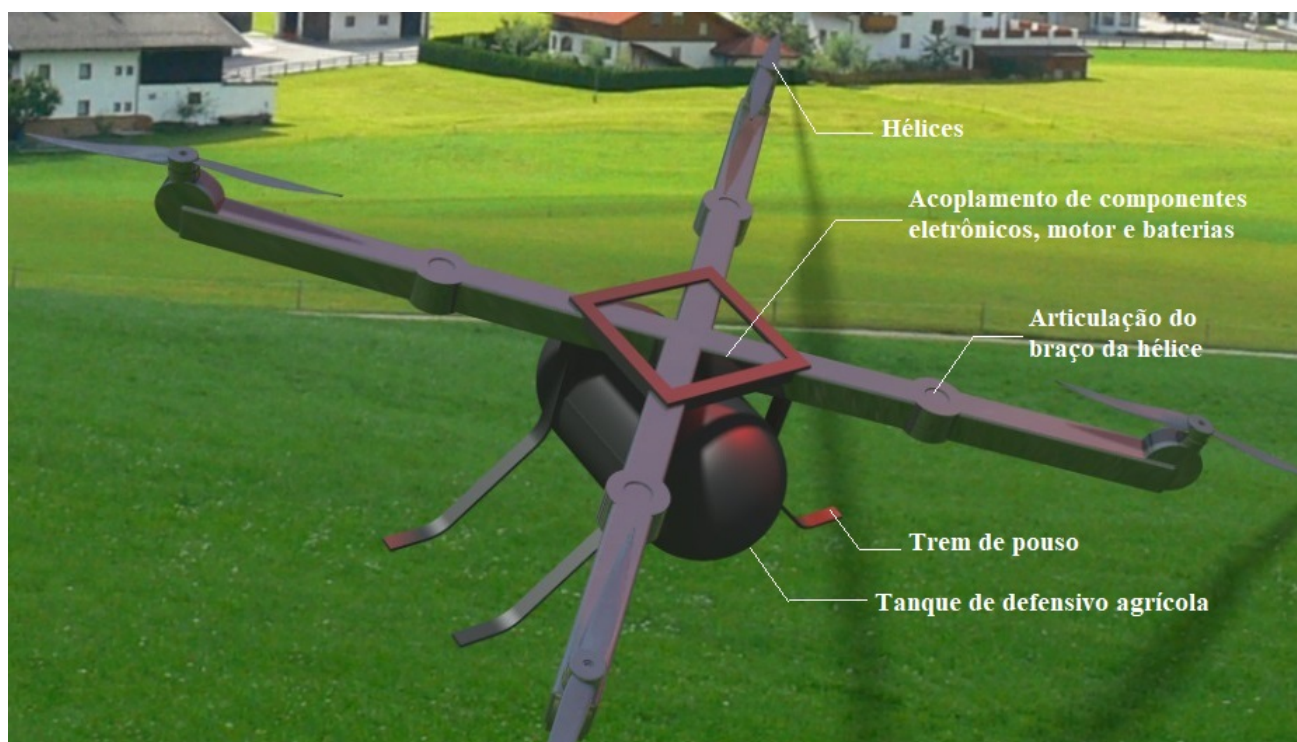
Vista isométrica e componentes mecânicos principais. Fonte: Autores
